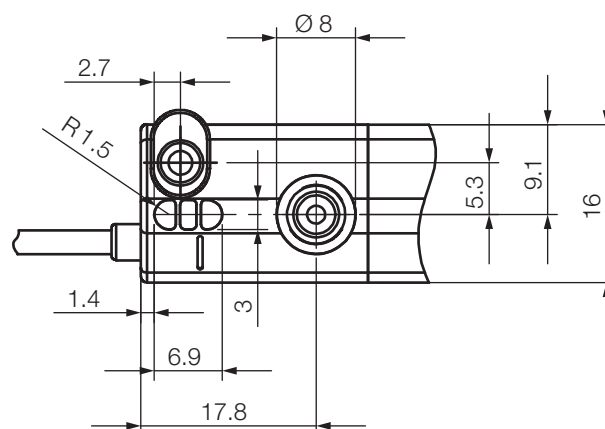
Dimensions et distances du bouton-poussoir et des LED
